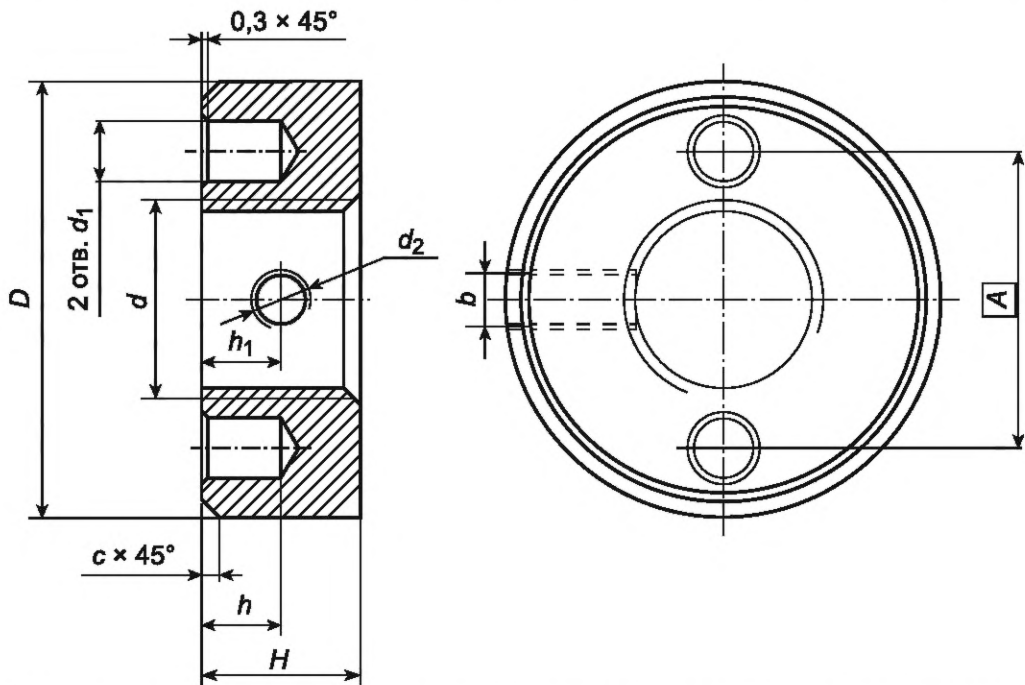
Конструкция круглых гаек с торцевыми отверстиями «под ключ» и отверстием для стопора
